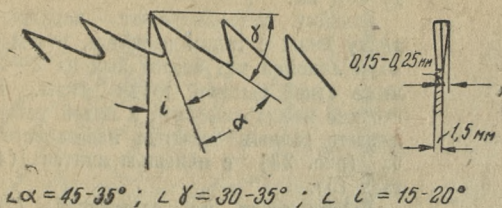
Профиль и угловые значения зубьев пилы для фрезерования
